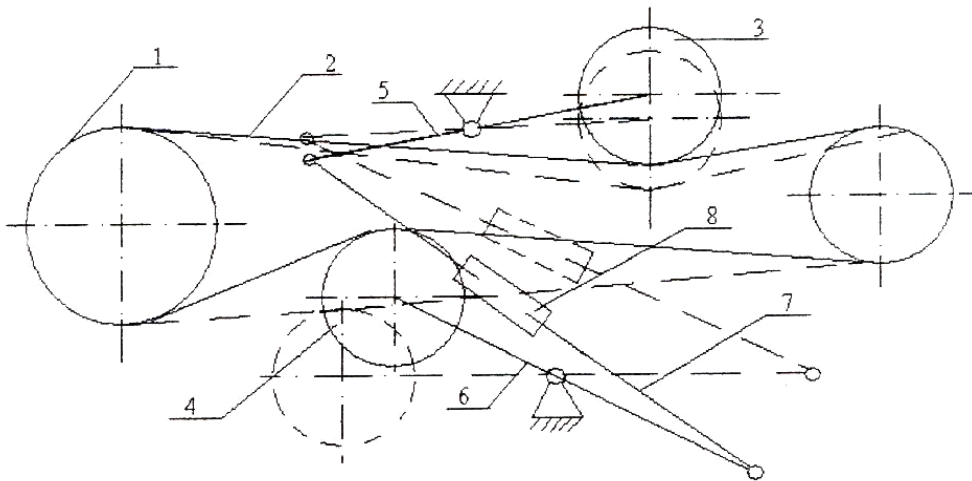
Триважільний натяжний пристрій для передач гнучкою ланкою сільгоспмашин:
